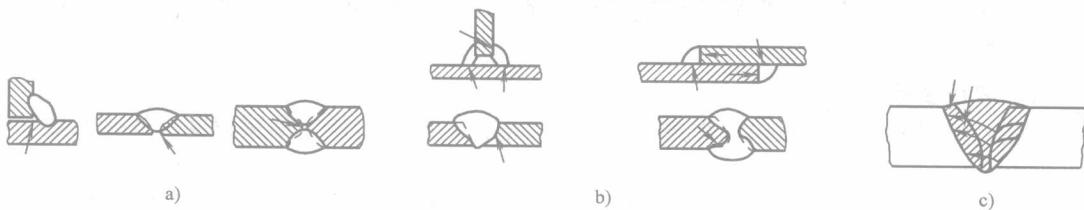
焊接电流过小容易产生的焊接缺陷
